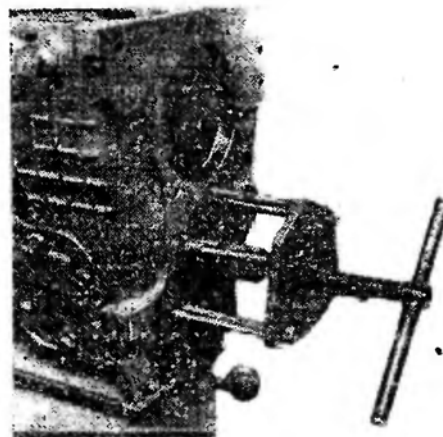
Запрессовка промежуточного вала в картер приспособлением
